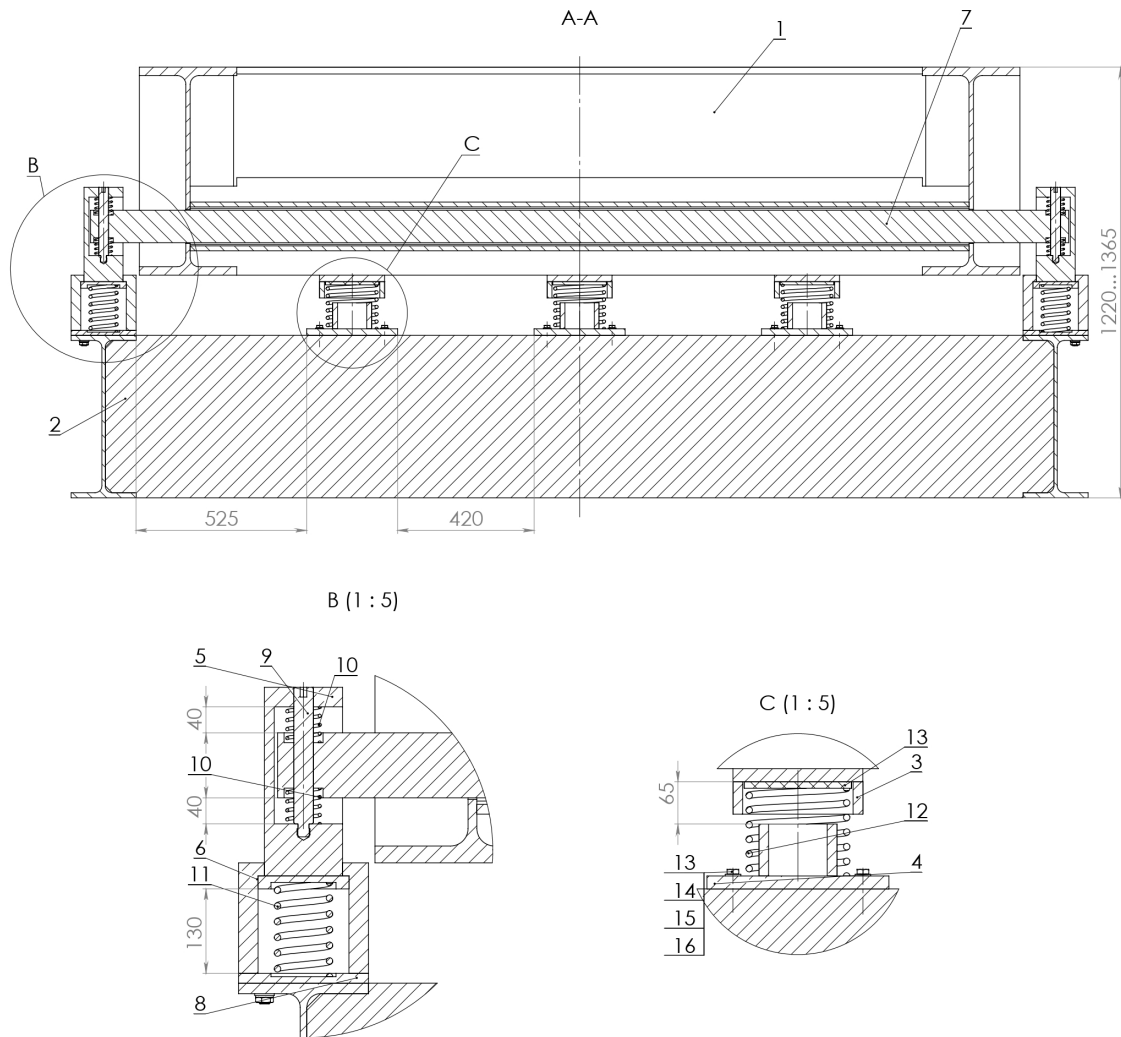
Конструкція удосконаленого демпферного механізму: 1 – рама пластинчастого живильника; 2 – рама демпферного механізму; 3 – верхній циліндр; 4 – основа циліндрична; 5 – стійка; 6 – гільза; 7 – поперечний елемент; 8 – основна пластина; 9 – направляючий стержень; 10, 11, 12 – пружини демпфування; 13 – прокладка гумова; 14 – болт; 15,16 – шайба; 17 – гайка
